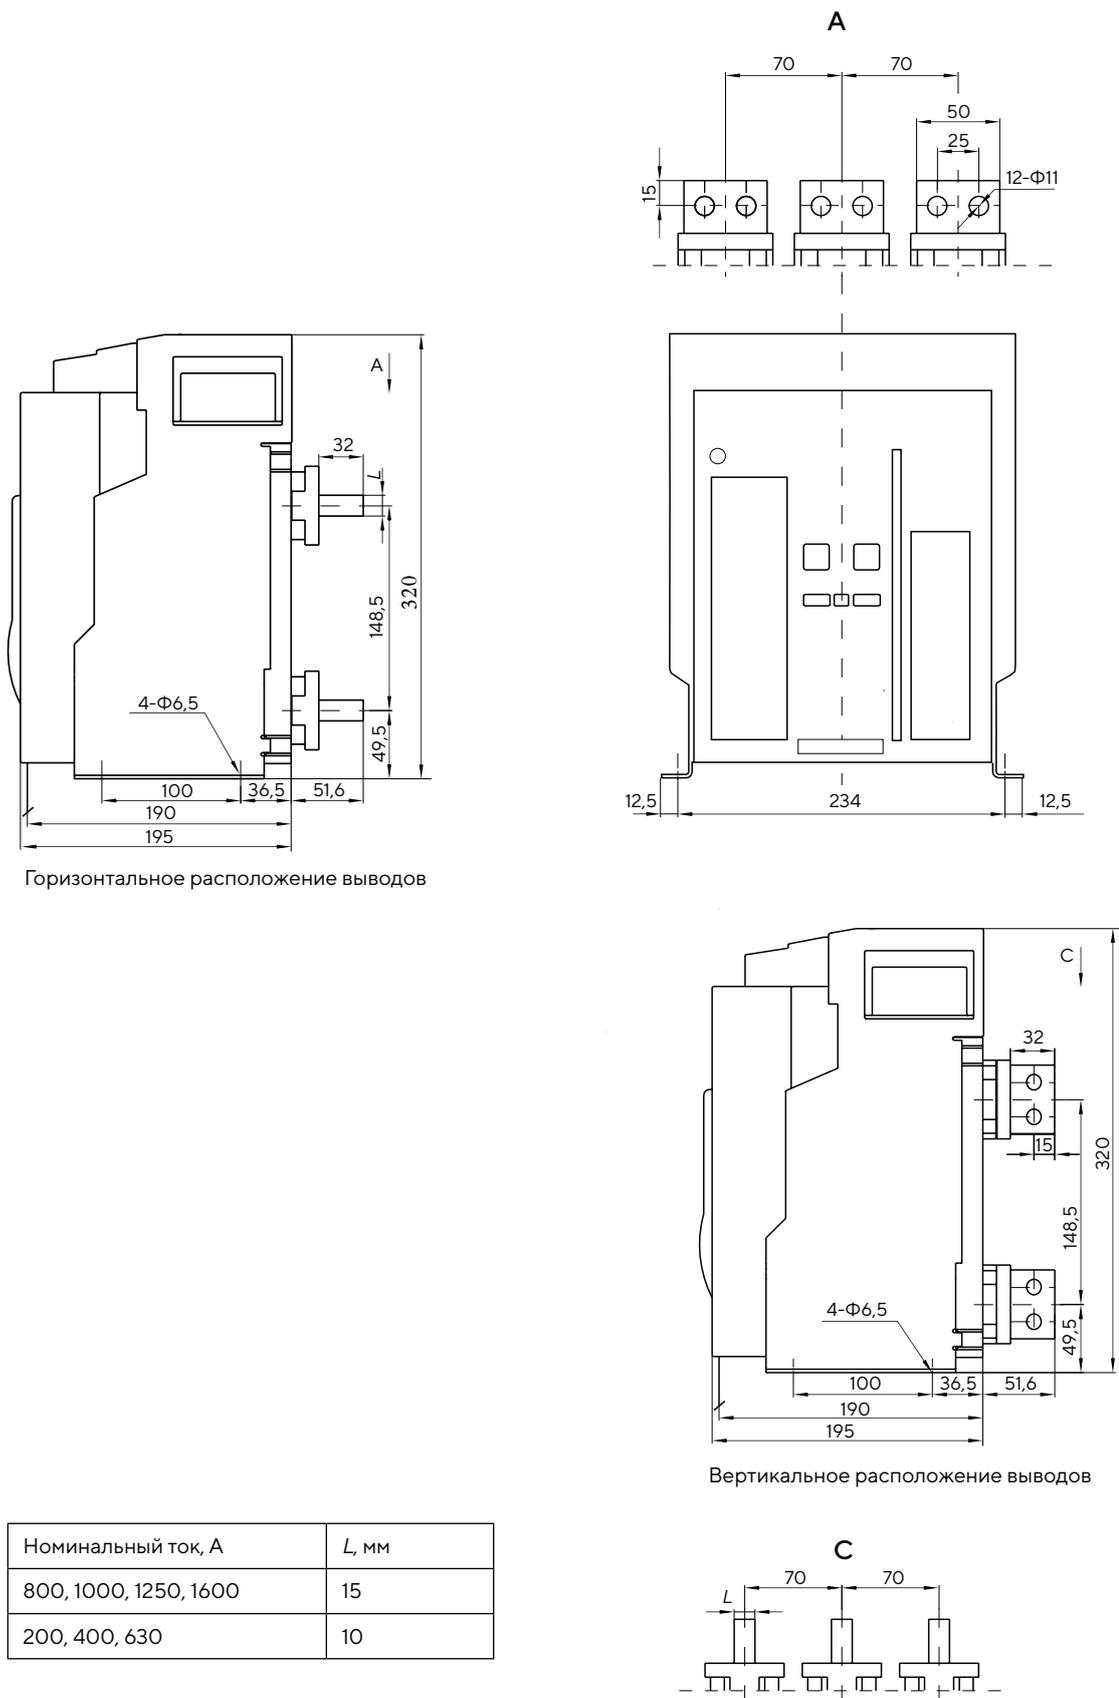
Габаритные размеры стационарных трехполюсных выключателей типоразмера А
